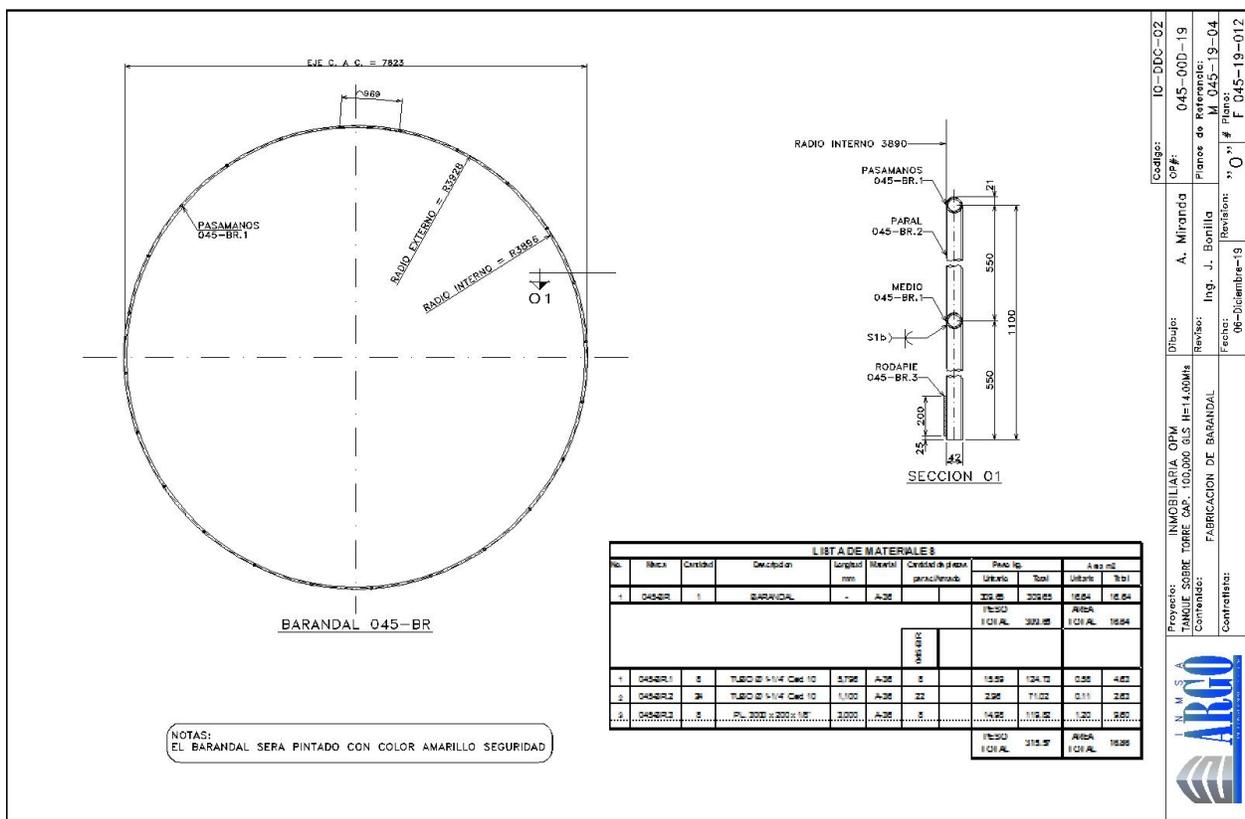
Plano de fabricación de barandal para tanque elevado
